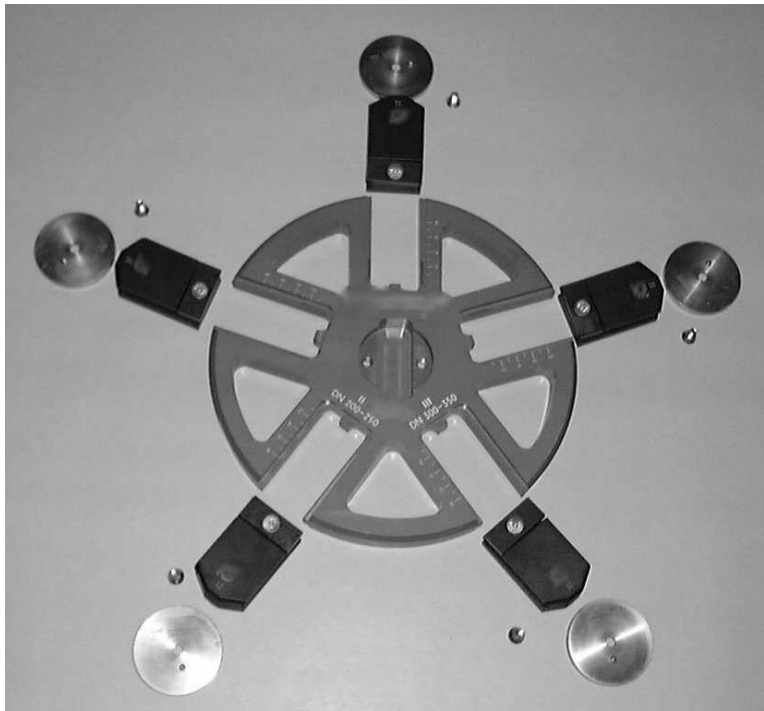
Детали инструмента для планетарного шлифовального колеса (изображен следующий вариант: диаметр планетарного колеса 220 мм, размер планетарных стержней II, диаметр шлифовальных кругов из КНБ 50 мм)
